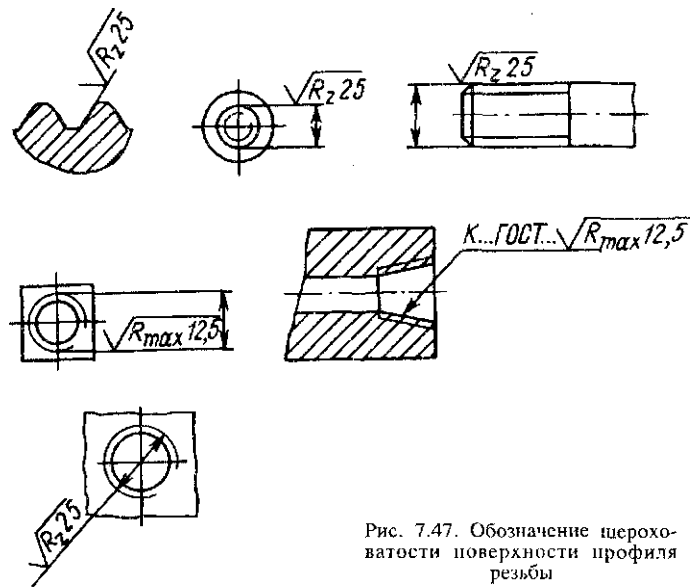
Обозначение шероховатости поверхности профиля резьбы
